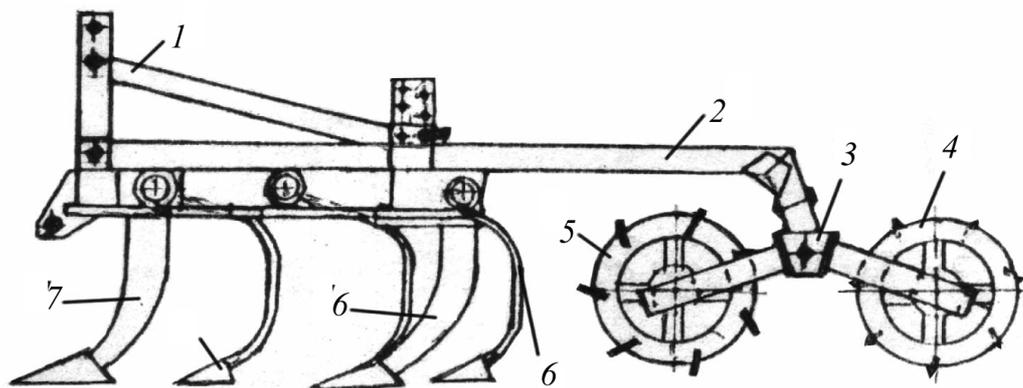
Почвообрабатывающий агрегат АКР-3: 1 – навесная система; 2 – рама; 3 – баланси́р катков; 4 – прикатывающий каток; 5 – каток-разравниватель; 6 – упругая лапа стрельчатого типа; 7 – жесткая стойка
